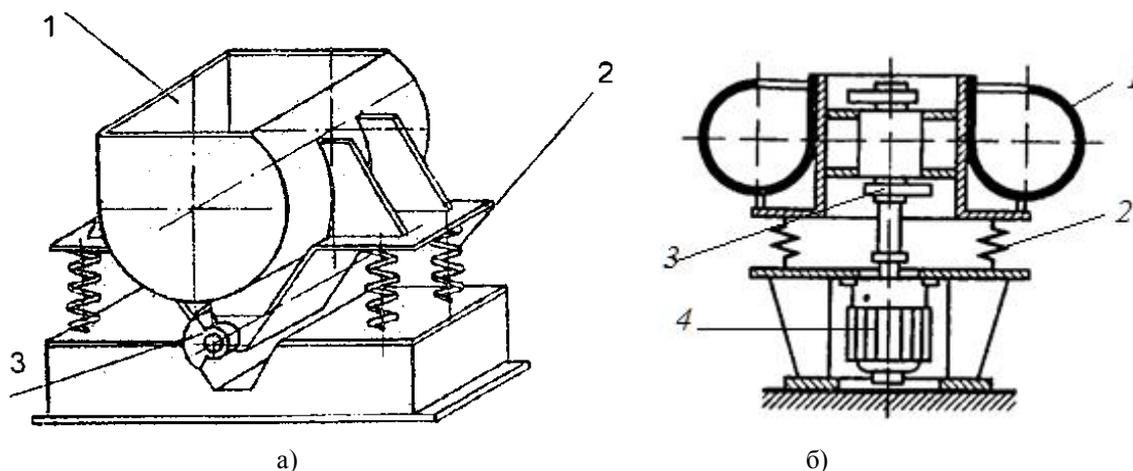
Вібраційні машини з дебалансними віброзбудувачами: 1 – робоча камера; 2 – пружини; 3 – дебалансний віброзбудувач; 4 – електродвигун; а – з U-подібною робочою камерою; б – з тороїдальною робочою камерою;
